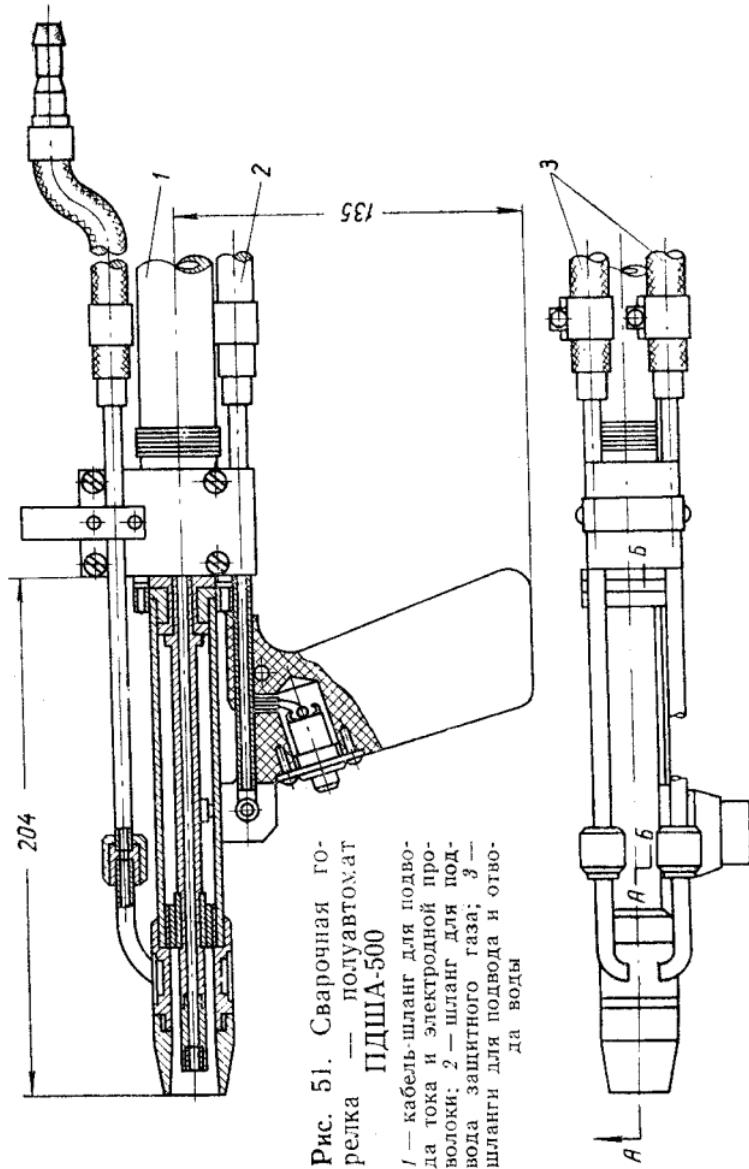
Сварочнаяго-релка ПДША-500
